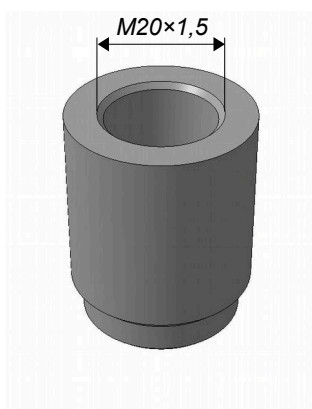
Вварная бобышка для крепежа преобразователя с помощью штуцера
